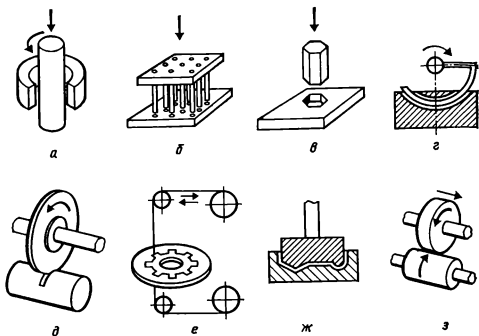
Форма инструментов для электроэрозионной обработки определяется производственными задачами и свободна от режущих зубьев со специальной геометрией; а — круглый пруток; б — набор стержней, проволоки; в — шестигранный пруток; г — дугообразный инструмент; д — дисковый; е — проволочный; ж — объемный, сложного профиля; з — цилиндрический
